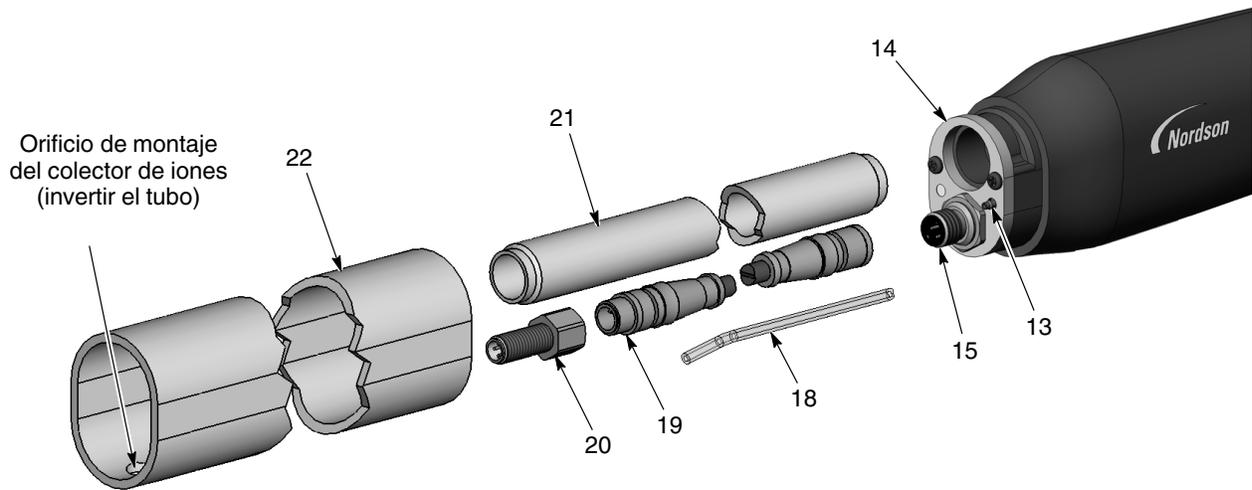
Desmontaje de la pistola de montaje en tubo 2 de 5
